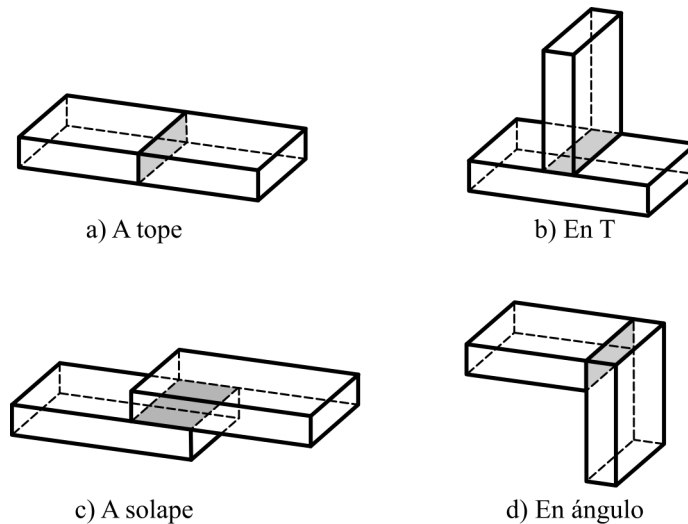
Tipos de juntas en las uniones soldadas
